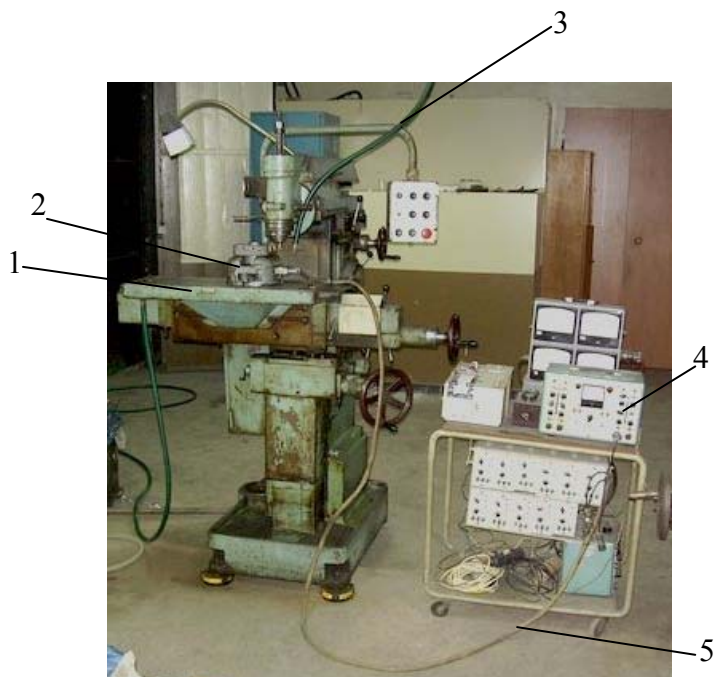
Общий вид стенда для проведения экспериментальных исследований (1 – фрезерный станок 6М76П-1; 2 – динамометр УДМ600; 3 – устройство принудительного удаления стружки; 4 – регистрирующий комплекс; 5 – линии передачи сигналов)
